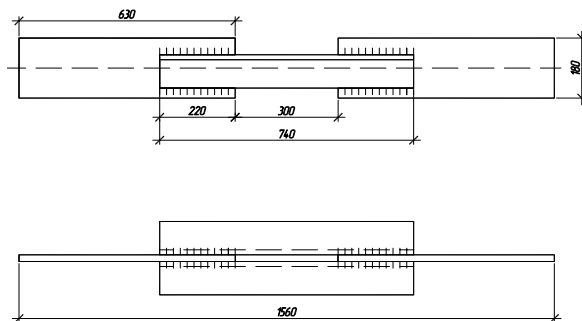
Сварное нахлесточное соединение из двух парных уголков
